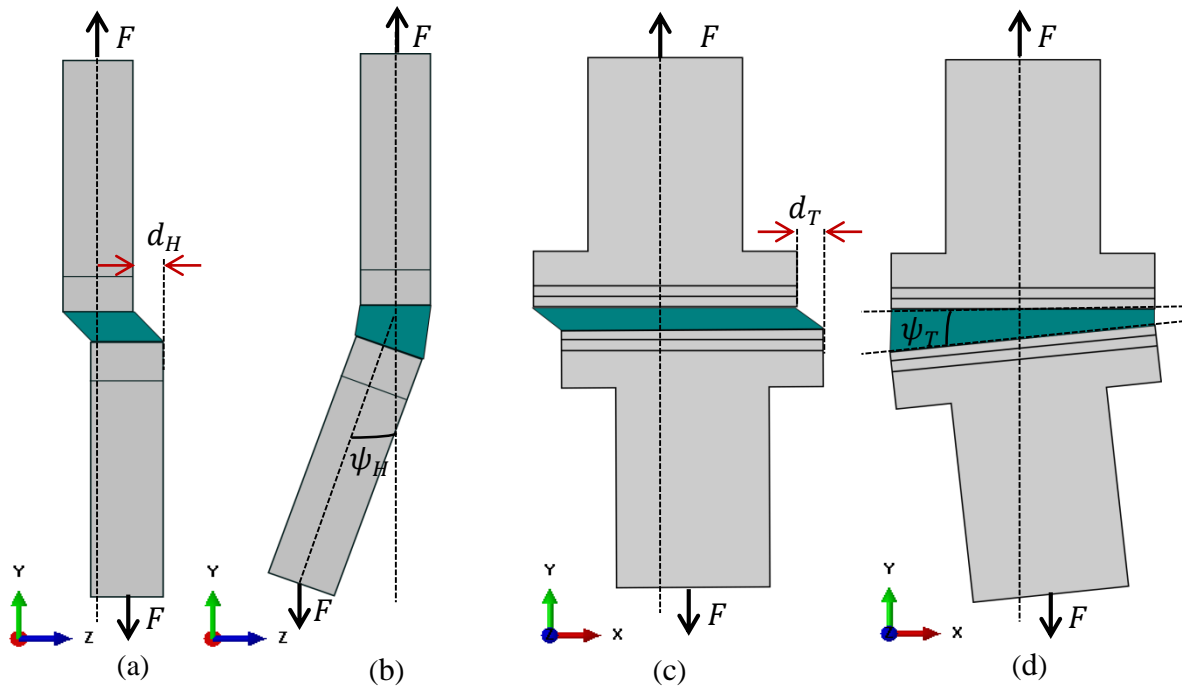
Défauts étudiés lors du collage des éprouvettes Scarf modifié.(a) défaut d'alignement hors plan, (b) défaut de parallélisme hors plan, (c) défaut d'alignement tangentiel, (d) défaut d'hétérogénéité de l'épaisseur du joint de colle.
